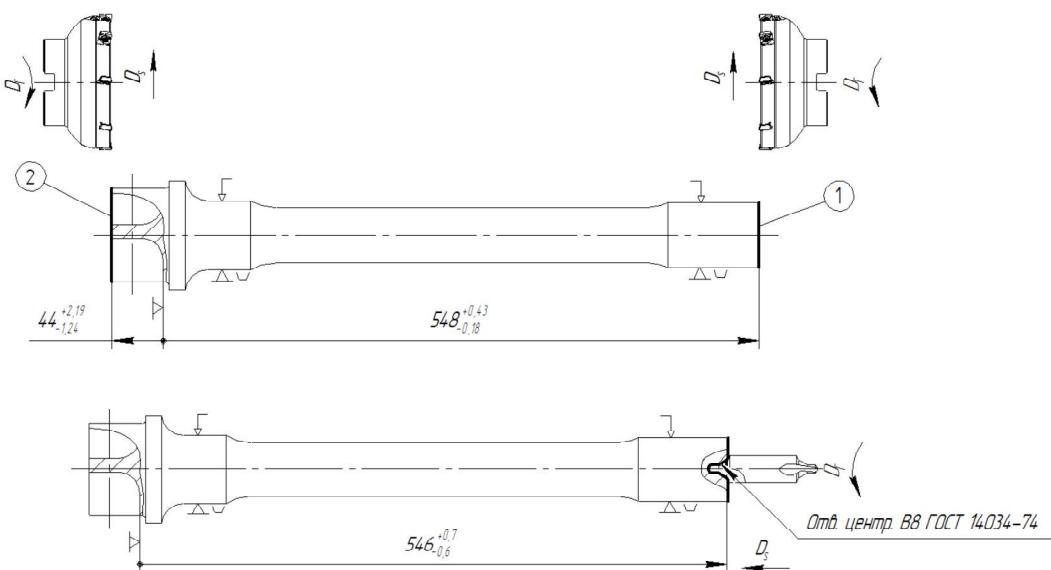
Операція 010 Фрезерно-центральна
